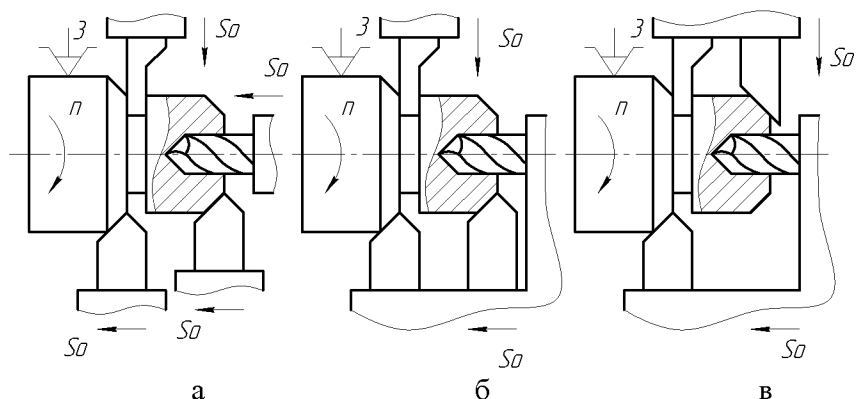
Схема обробки валика на: а - токарно-гвинторізному верстаті (І клас), б - токарно-револьверному верстаті (ІІ клас), в - токарному багаторізцевому напівавтоматі (ІІІ клас)
